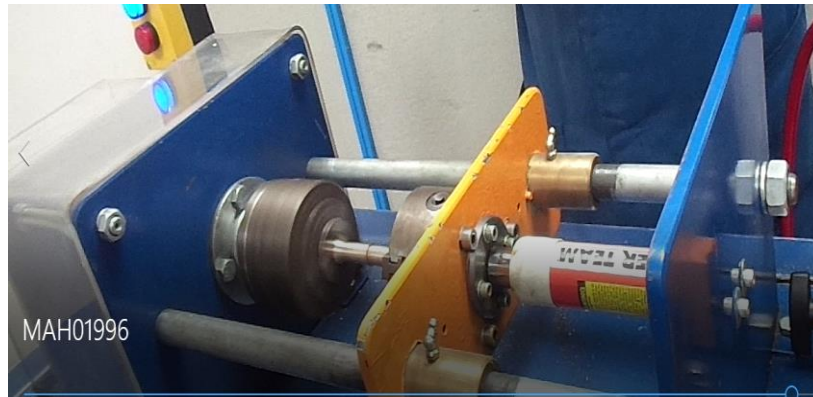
Soldadura por fricción del bronce SAE 40
